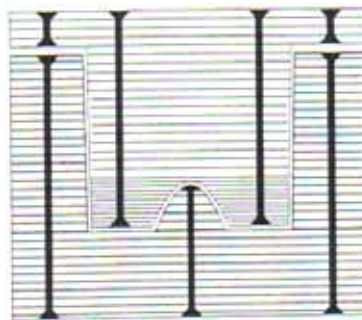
Assemblage de strates par vissage [Dickens 97]
